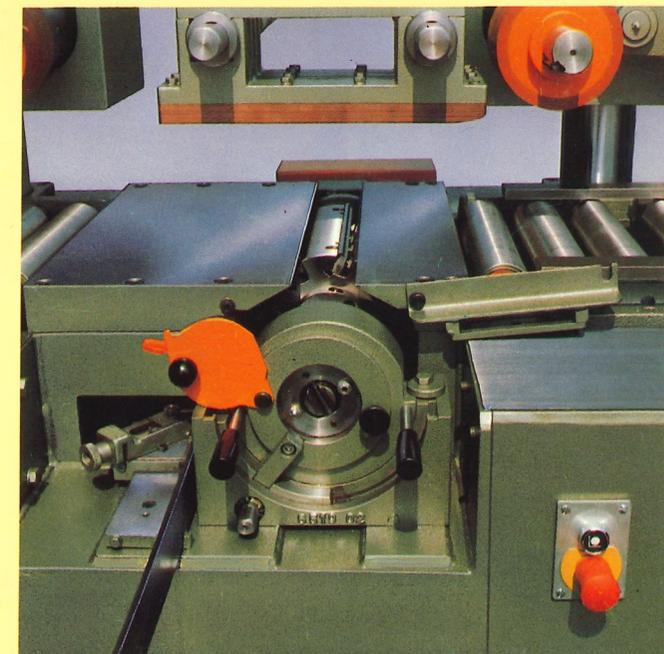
Rotaplanwelle mit Hydrowerkzeugen
